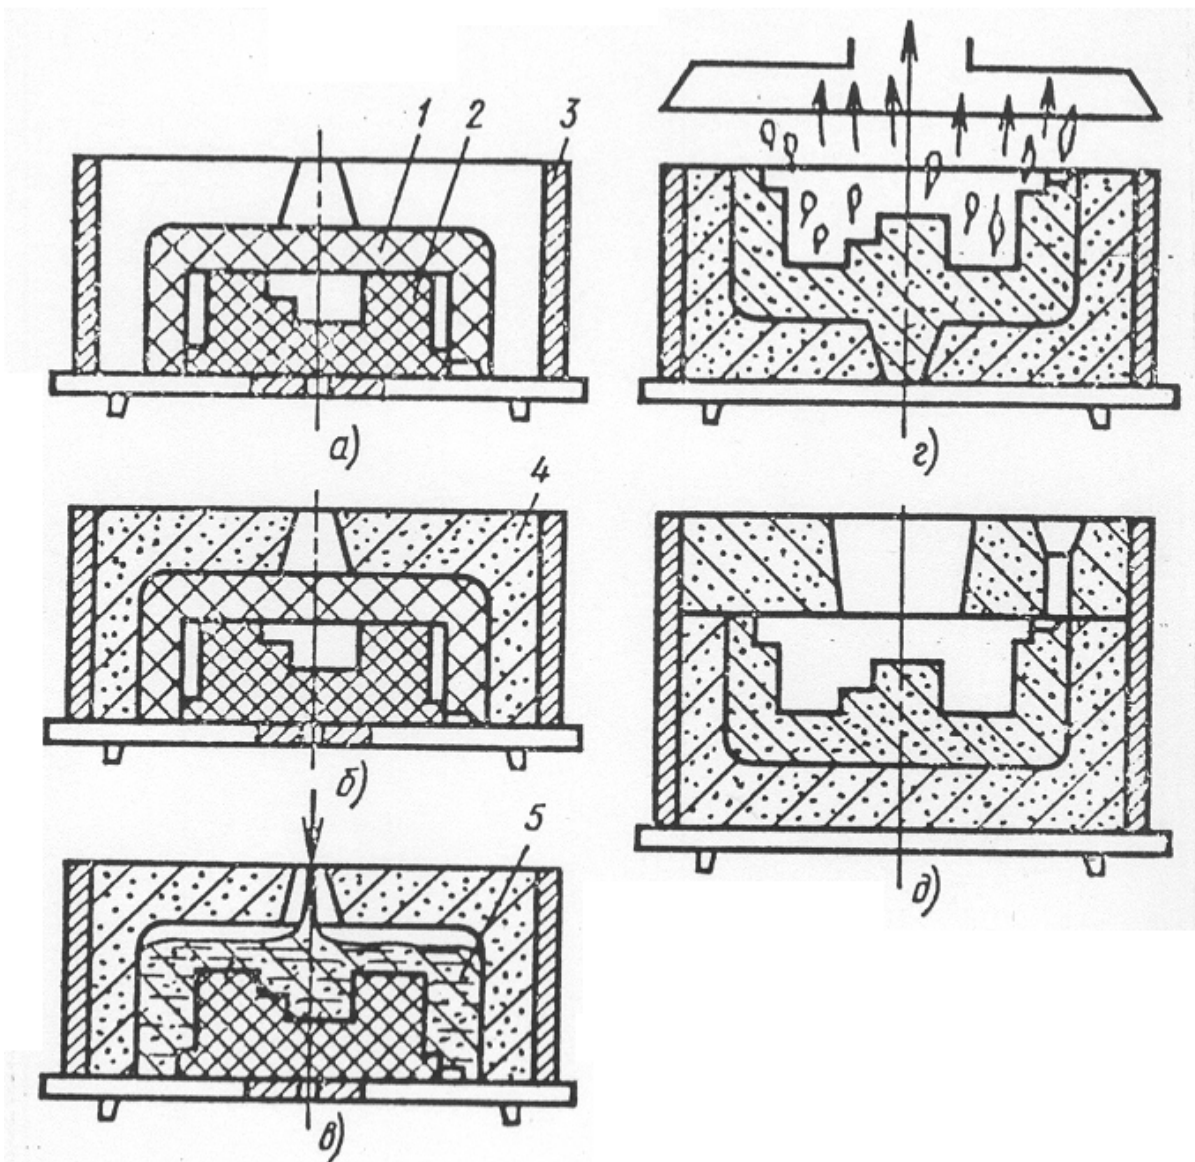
Последовательность изготовления объемной керамической формы: а – установка модельного комплекта; б – заливка наполнительного слоя формы (ЖСС); в – заливка облицовочного слоя из огнеупорной суспензии; г – удаление растворителя; д – собранная и готовая к заливке форма; 1 – вспомогательная модель; 2 – модель оливки; 3 – опока; 4 – наполнительный слой формы (ЖСС); 5 – облицовочный слой (ЭТС).
